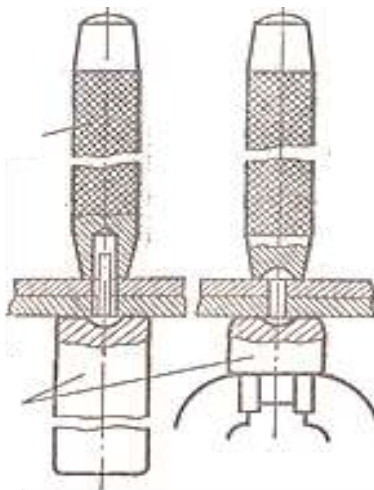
Инструменты для клепки: 1- поддержка, 2- натяжка, 3- обжимка
